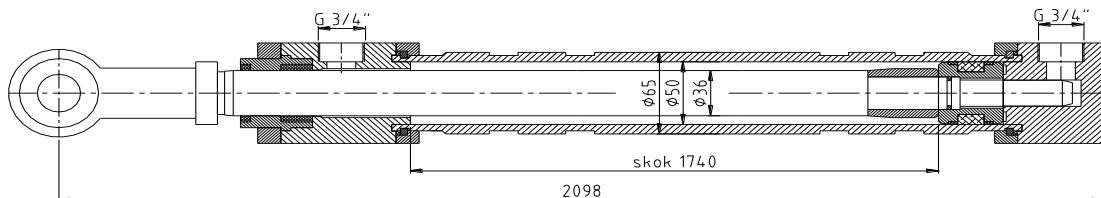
Modulzylinder mit Gelenkkopf GIKFR.
